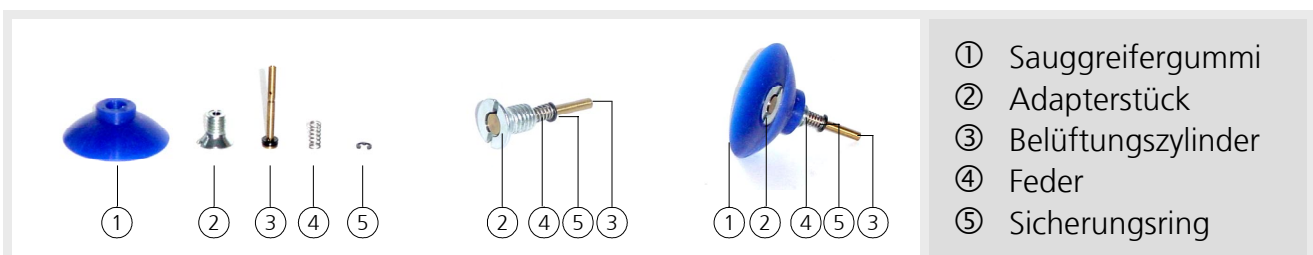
Aufbau des passiv betriebenen Sauggreifers mit integriertem Ventil
